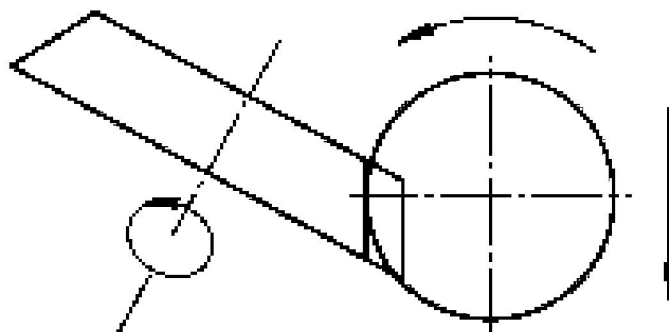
Схема обработки эвольвентно-конического колеса цилиндриконической передачи
